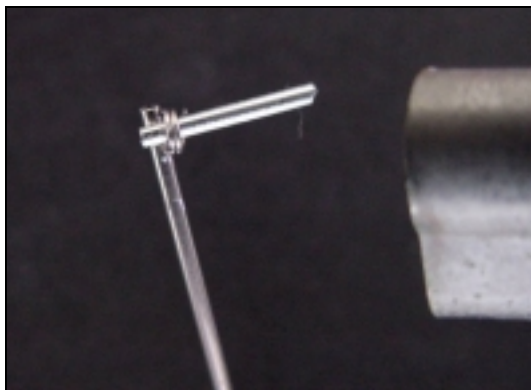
Insira duas espiras de solda de prata no segmento mais curto dos dois tubos soldados e use um maçarico para soldar definitivamente as duas partes
